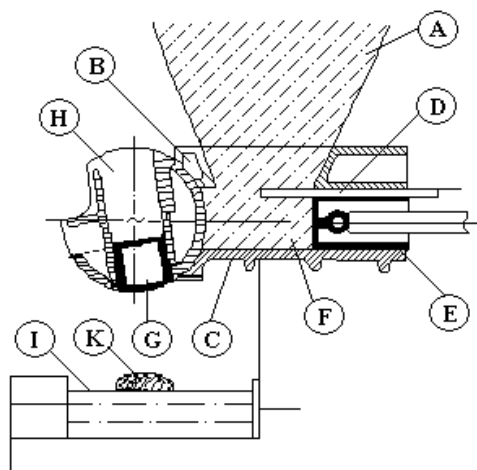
Вакуумное делительное устройство барабанного типа: А – бункер; В – воронка бункера; С – корпус всасывающей камеры; D – заслонка (делительный нож); E – нагнетательный поршень; F – всасывающая камера; G – дозировочный (мерный) поршень; H – мерная камера задней заслонки (барабана); I – конвейерная лента; K – порция теста
